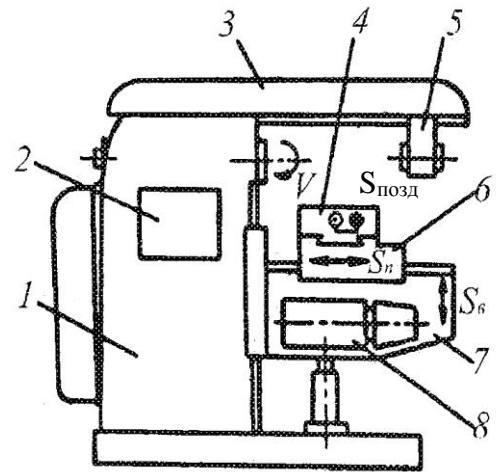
Загальний вид горизонтально-фрезерного верстата
